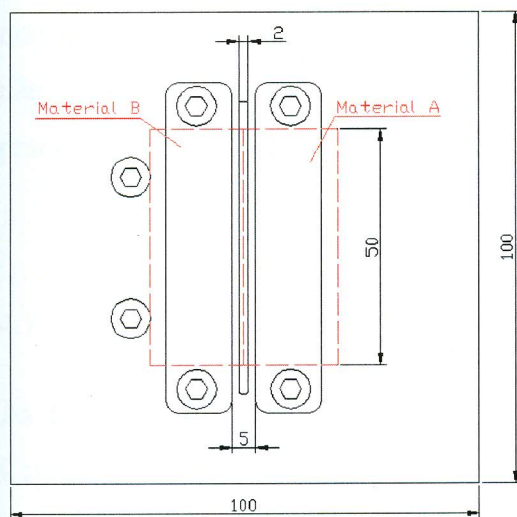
Dispositivo de posicionamento e fixação para o experimento de solda laser.
